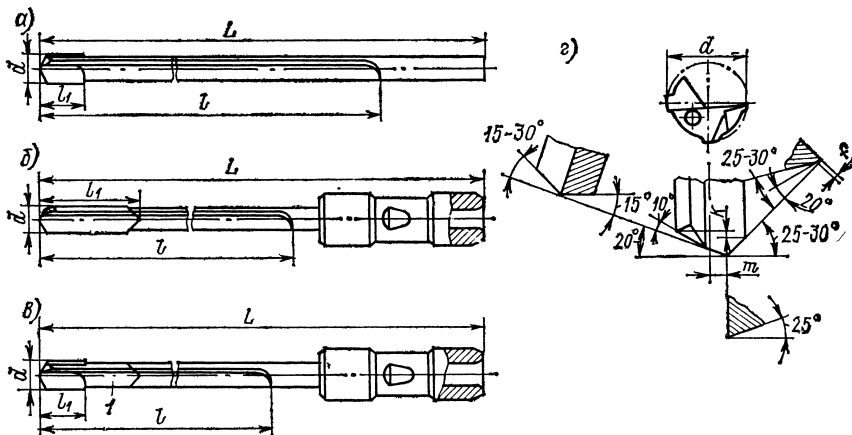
Сверла одностороннего резания: а — трубчатые с пластинкой твердого сплава; б — то же, но с цельной твердосплавной рабочей частью; в — то же, но с креплением пластинки к промежуточной головке  $l$ ; г — форма заточки вершины
